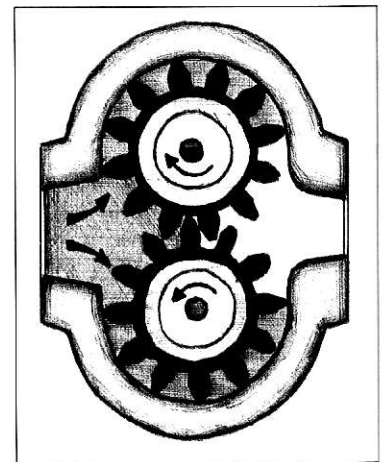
Ejemplo de bomba hidráulica "de engranaje".
